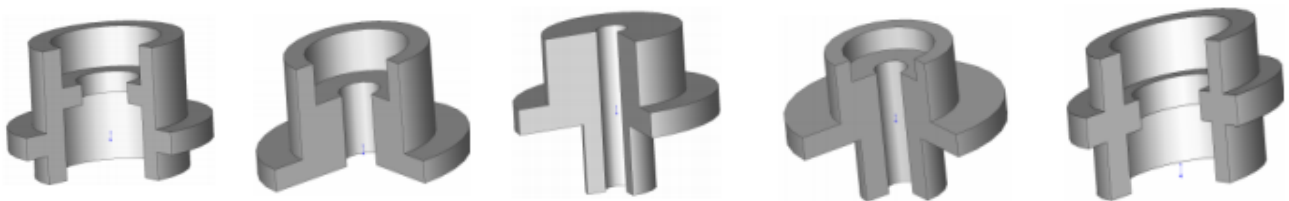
Заготовки, полученные способом комбинированного выдавливания
